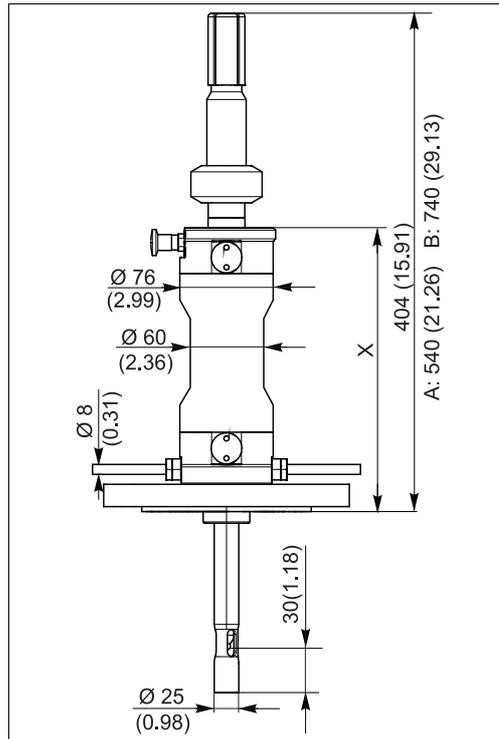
Version : standard, pour capteurs à remplissage gel.
